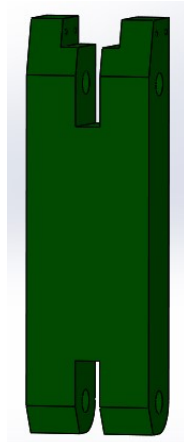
Viga vertical sin pistones (Fuente: propia)
